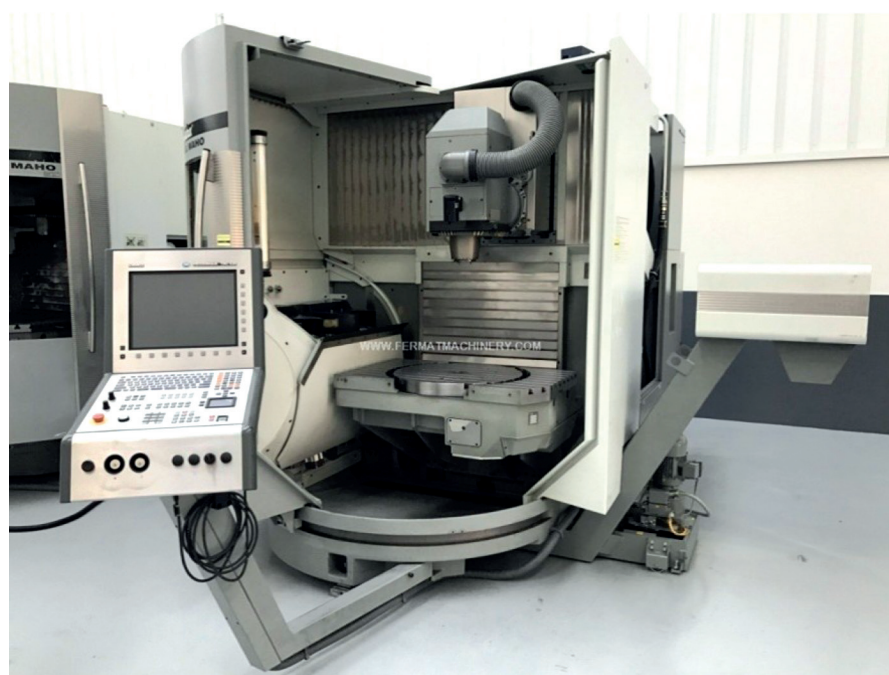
Высокопроизводительный фрезерный обрабатывающий центр DMU-60.
